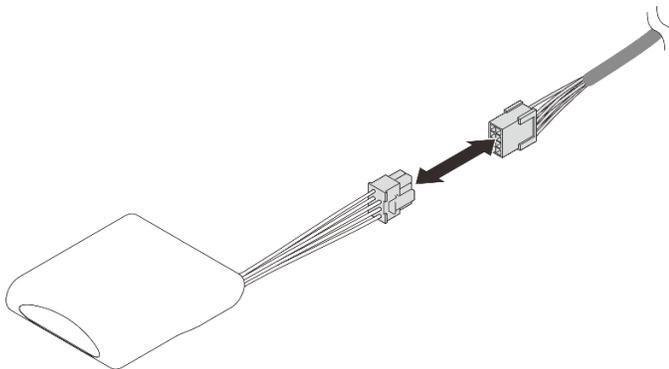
Collegamento del cavo del modulo di alimentazione flash
